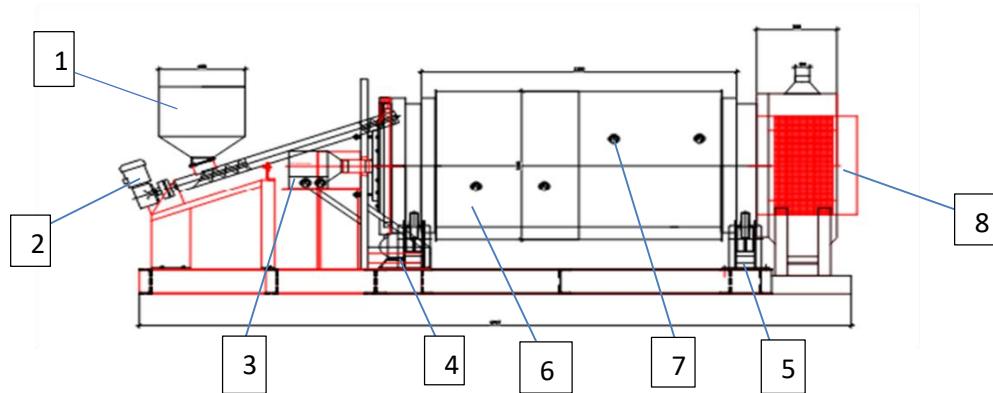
Сборочный чертеж опытно-промышленного биореактора:
